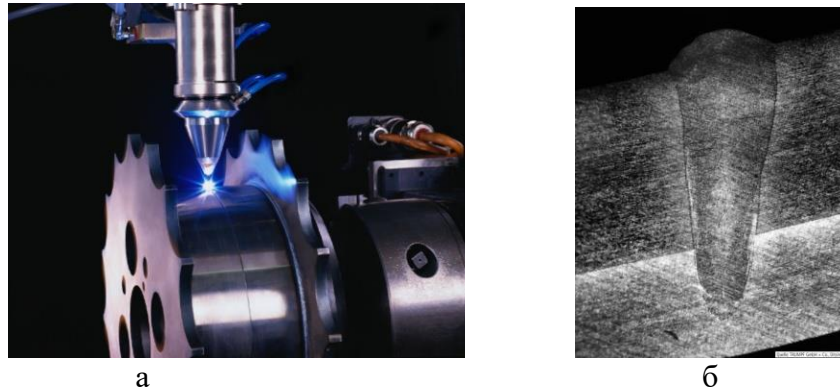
Лазерне зварювання: а) процес обробки; б) шов, що утворюється
